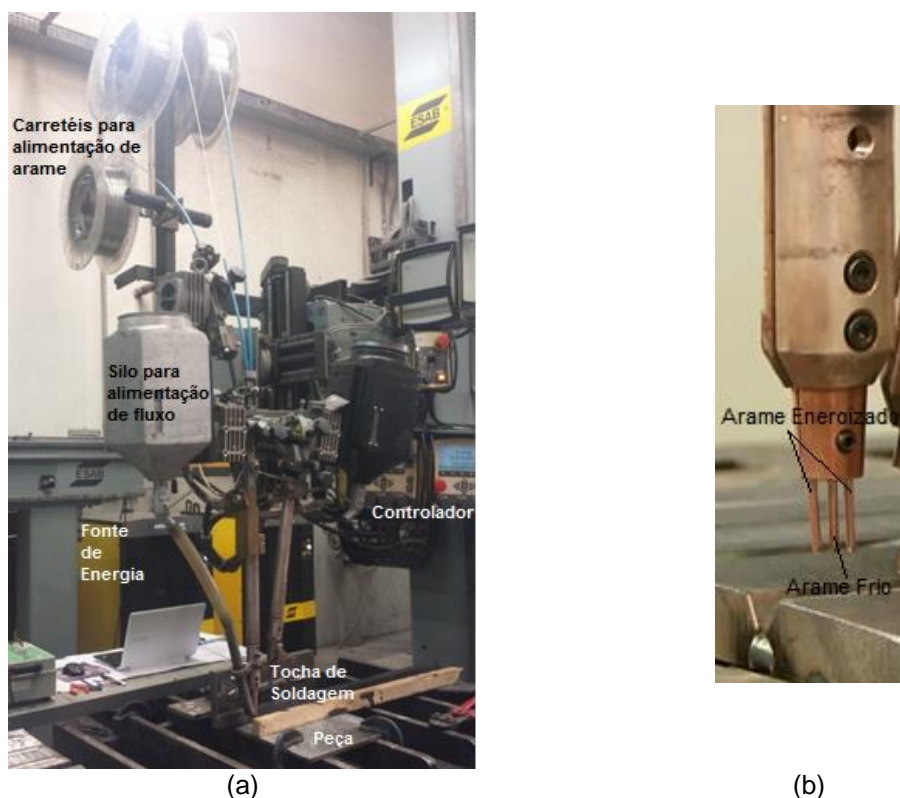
(a) Equipamento de Soldagem SAW Ice™ (b) Detalhe da tocha de soldagem
